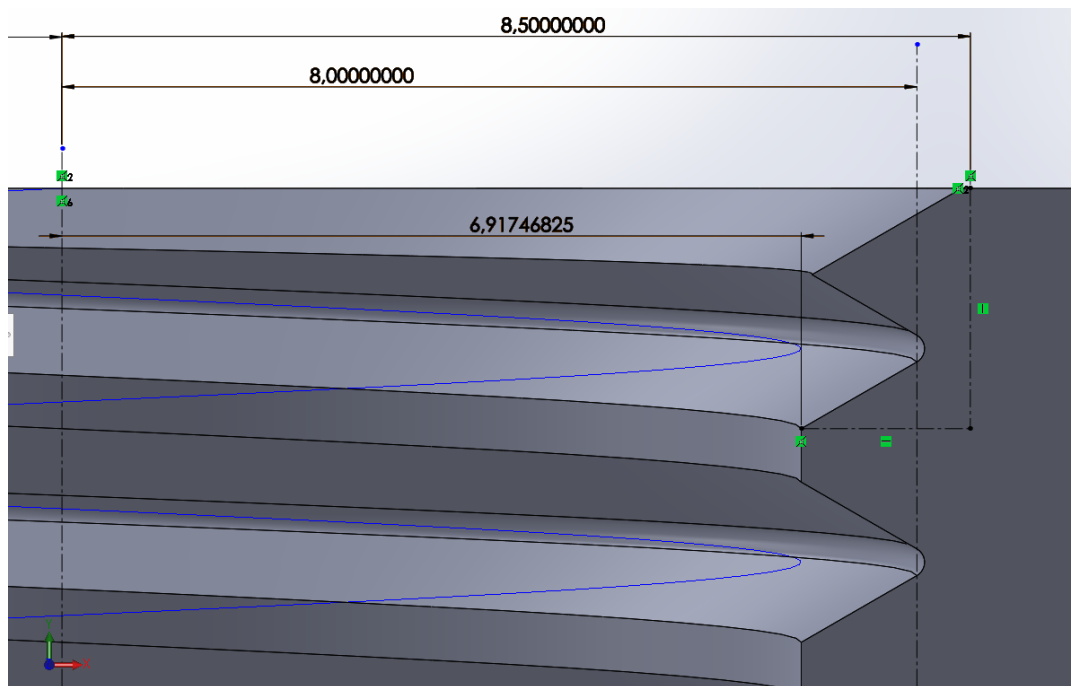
Croquis para comprobar las dimensiones del chaflán de la tuerca.
